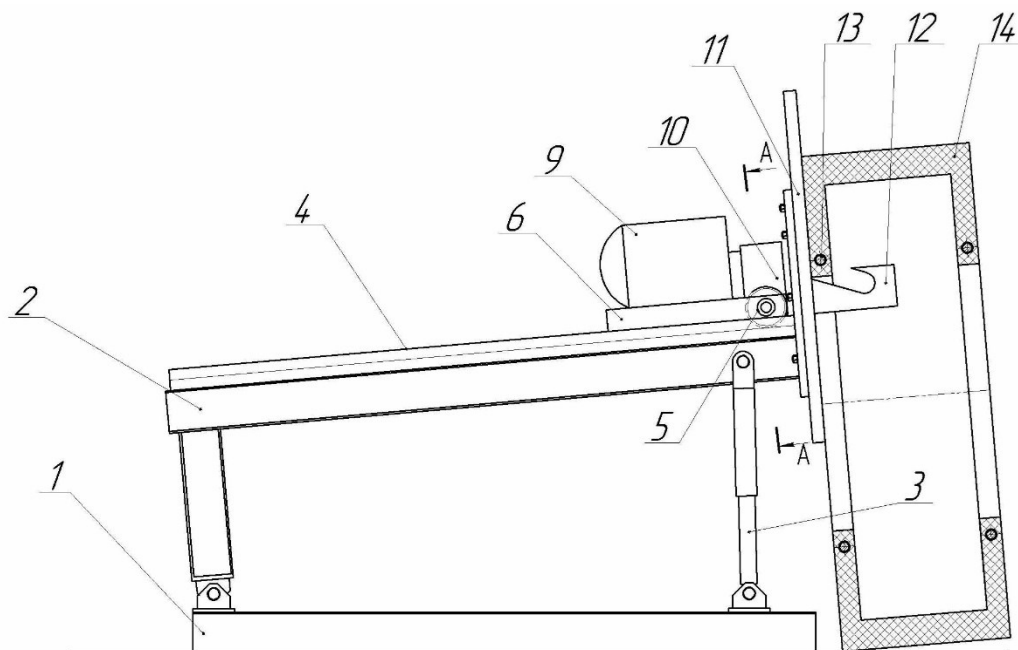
Общий вид установки для удаления троса из боковой части шины
